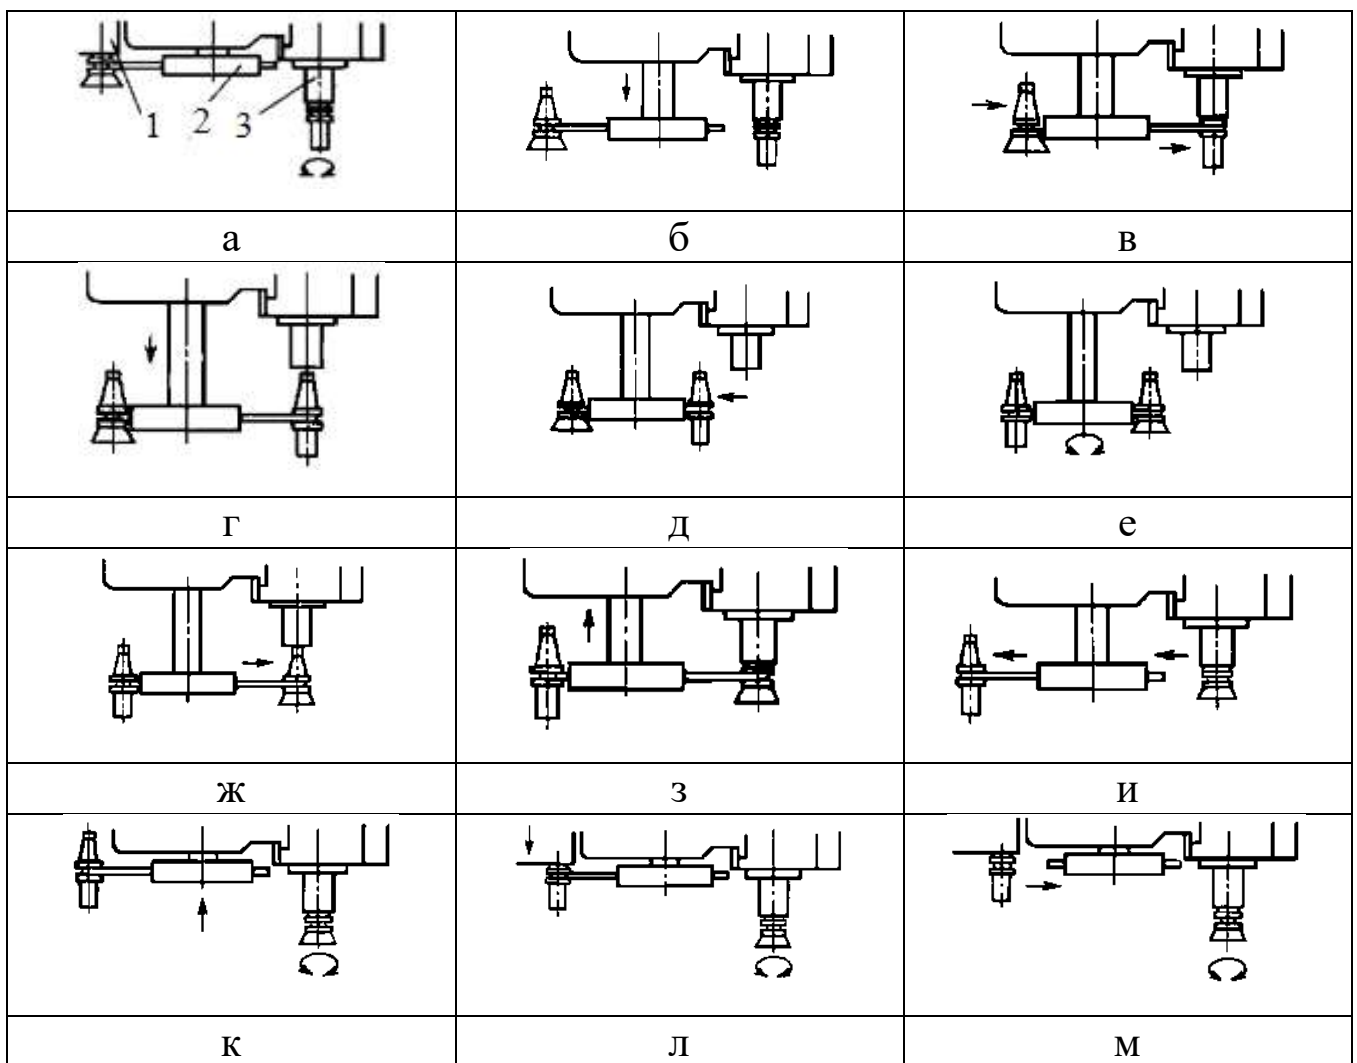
Послідовність зміни інструмента на верстаті з вертикальною компоновкою шпинделя: а, б – захват автооператором нового інструмента і виведення його із гнізда магазину; в, д – захват автооператором використаного інструмента і виведення його із посадочного отвору шпинделя; е – поворот автооператора на 180°; ж, з – установка нового інструмента в шпиндель станка; и, л – установка використаного інструмента в магазин; м – установка автооператора в вихідне положення
